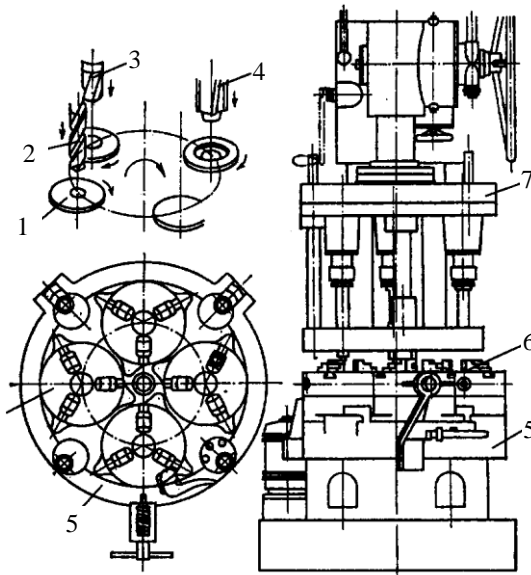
Схема обробки отворів тришпindelною голівкою на свердильному верстаті з поворотним столом:
